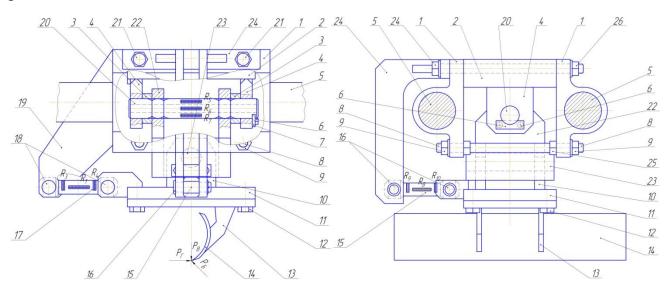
Схематичное изображение тензометрической головки: 1 — ползун; 2 — рама; 3 — втулка; 4, 10 — проушины; 5 — направляющие; 6, 12, 21 — болт; 9, 25, 26 — гайка; 7 — пластина; 8 — шпилька; 11 — основание; 13 — держатель; 14 — модель рабочего органа отвального типа; 15 — тяга регистрирующая боковую составляющую; 16, 18 — палец; 17 — тяга регистрирующая горизонтальную составляющую; 19, 24 — кронштейны; 20 — тяга регистрирующая вертикальную составляющую; 22 — П—образный консольный элемент; 23 — палец
